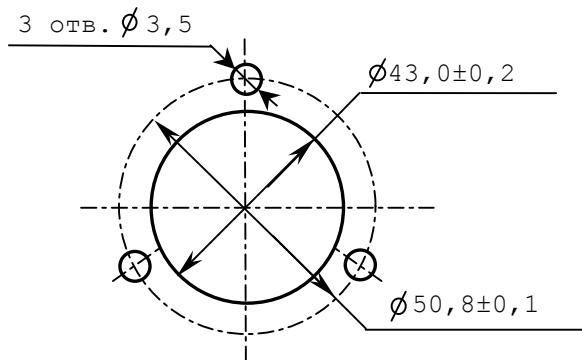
Установочные размеры штурвала ZBG-5-003-100
